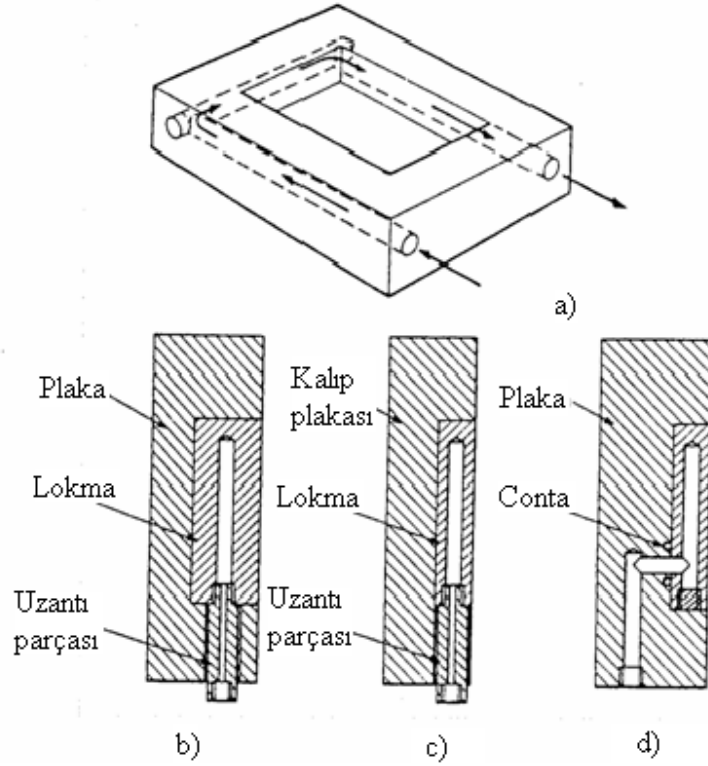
Dikdörtgen kalıp plakası soğutma devresi gösterilmiştir
